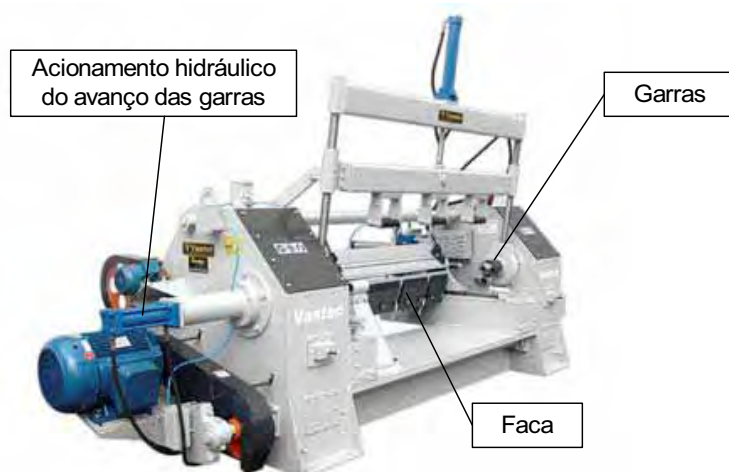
Torno laminador com garras. Fonte: VANTEC.
